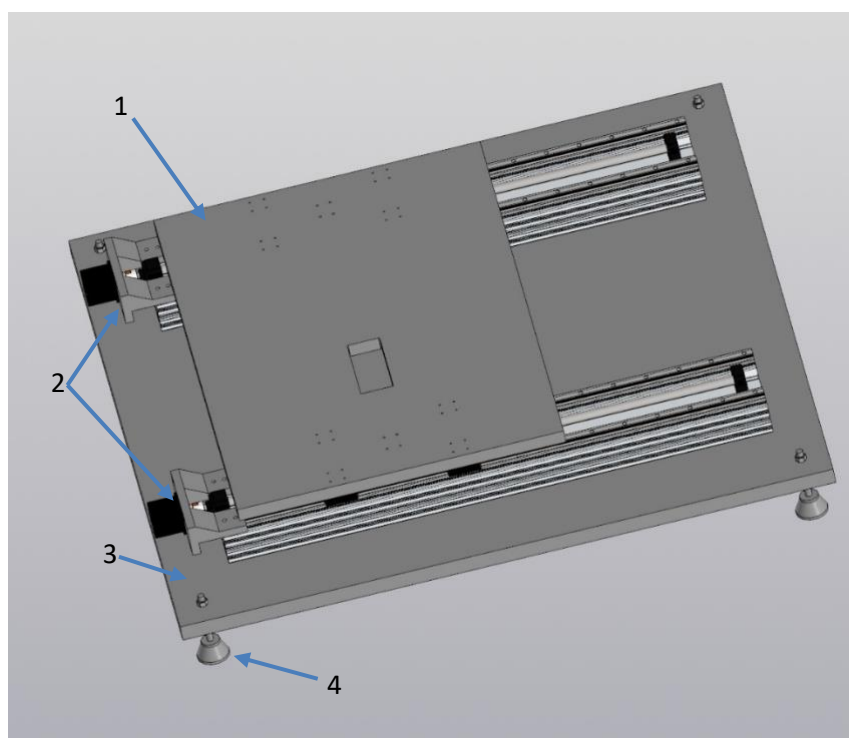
Привод оси x: 1 – Полка; 2 – Линейный привод;
